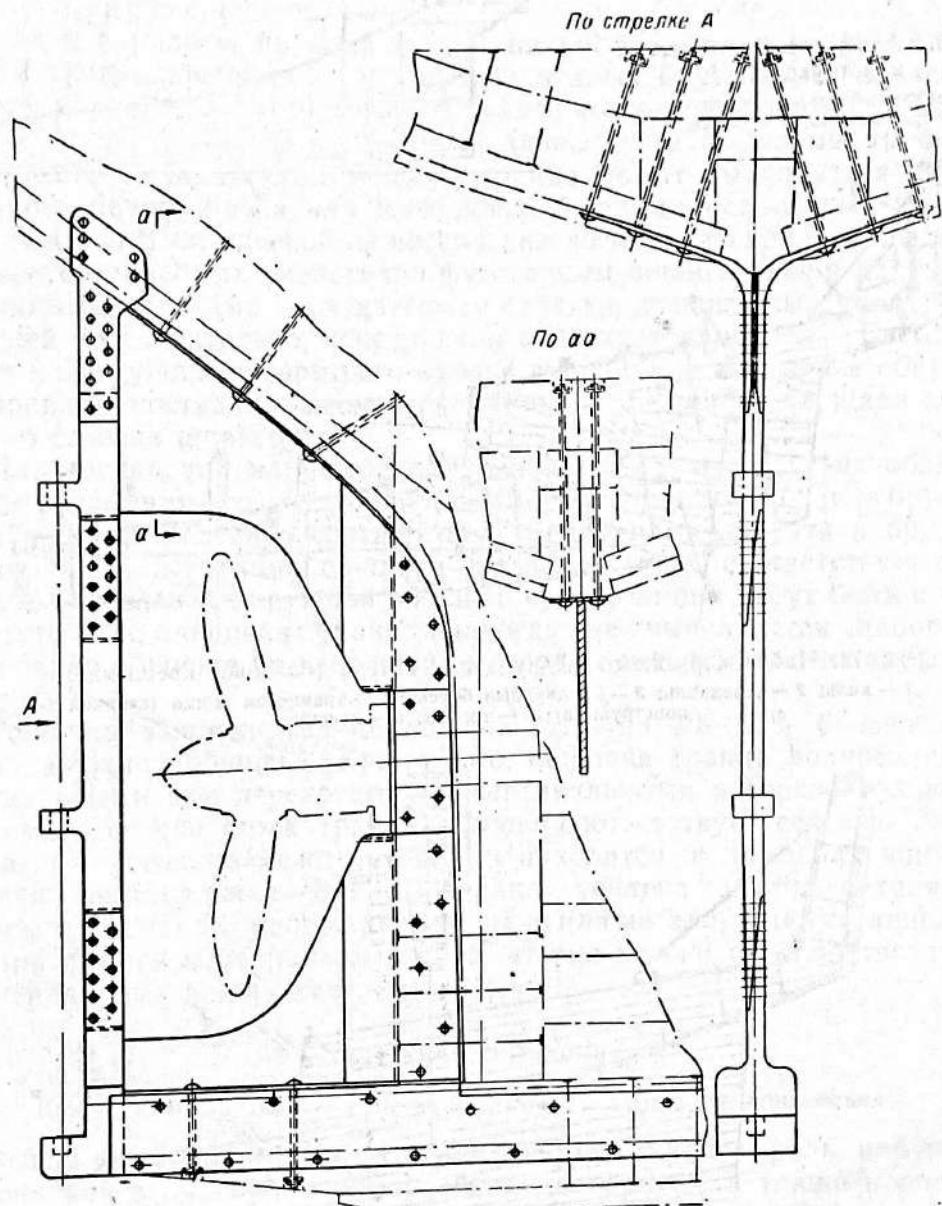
Крепление стального рулерпоста к корпусу судна.
